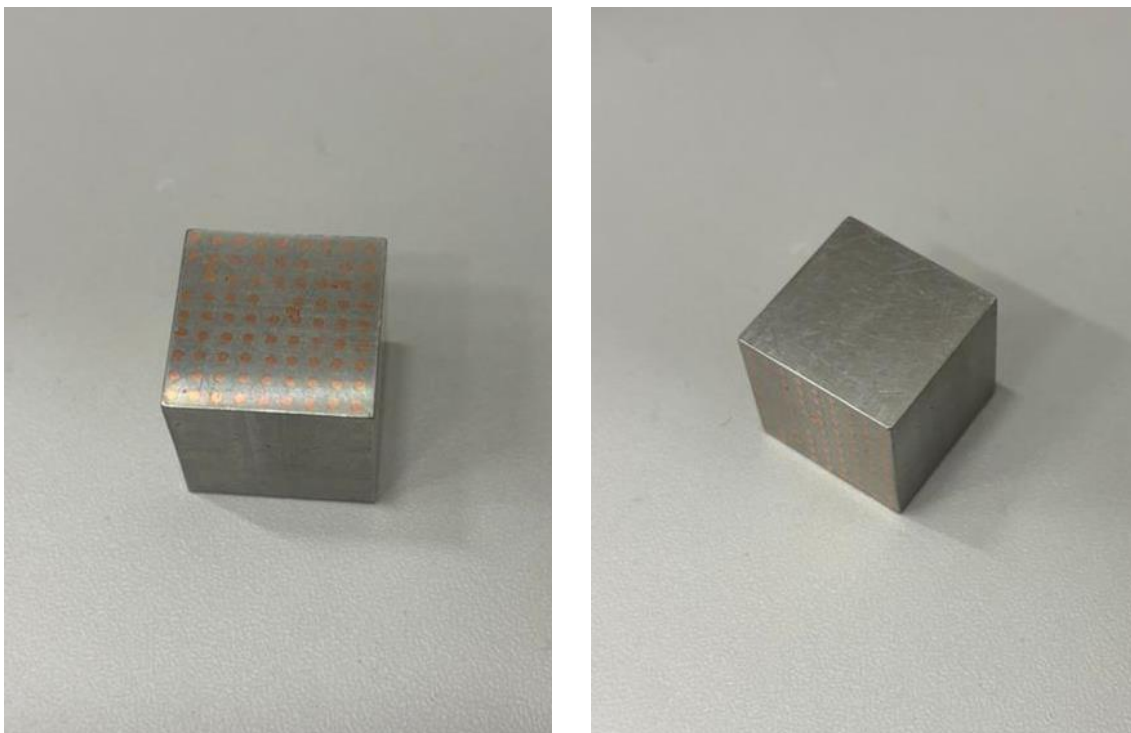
Модельный биметаллический образец ПОС-61 + Cu с однонаправленным медным наполнителем
